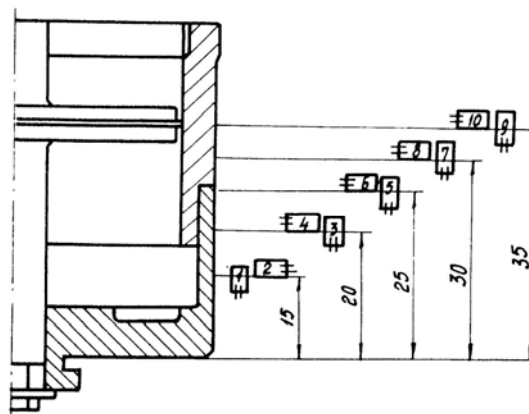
Схема установки тензодатчиков на наружной поверхности корпуса гидроцилиндра
